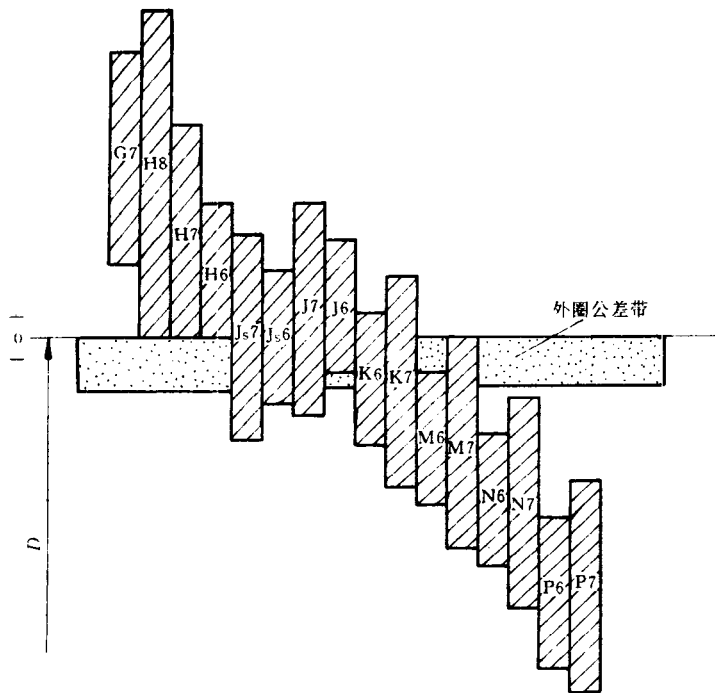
与滚动轴承配合的外壳孔的常用公差带
